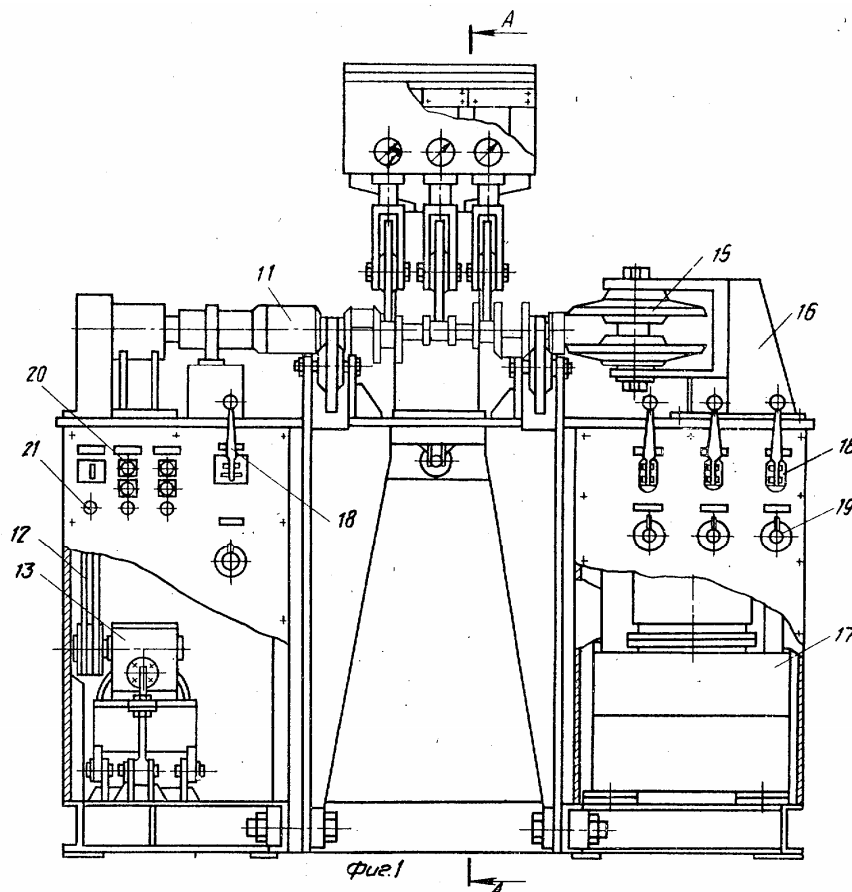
Пресс для правки коленчатых валов (RU 1388140)
